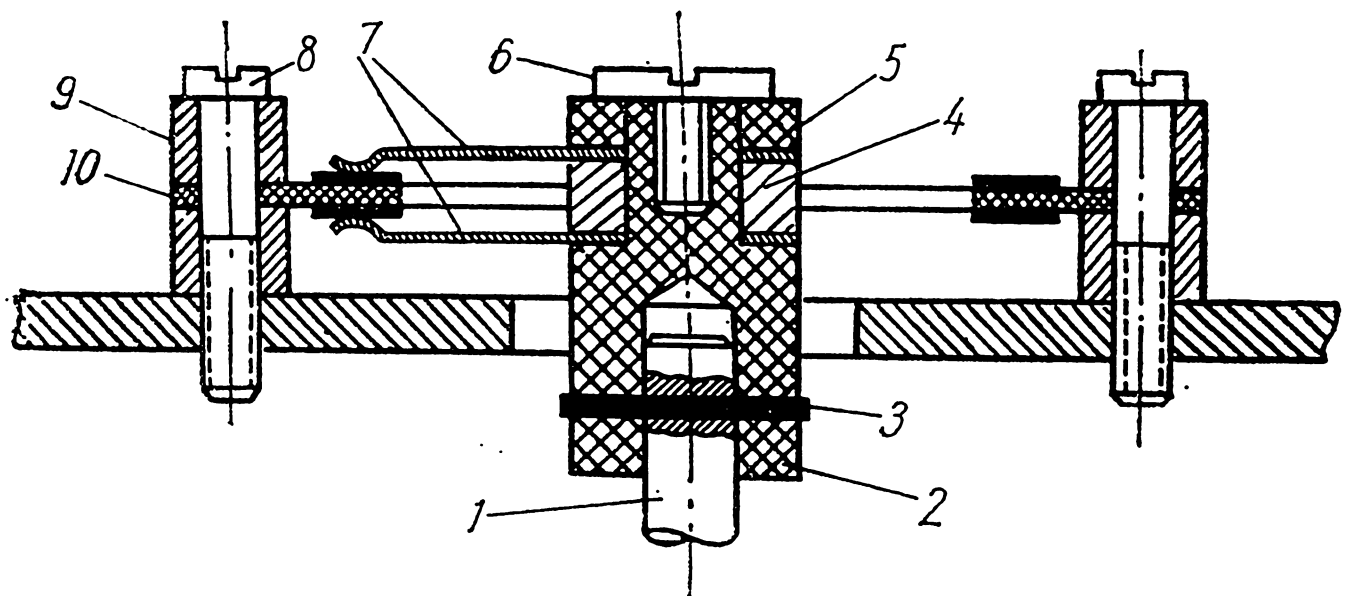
Механізм комутатора: 1 — вісь редуктора електродвигуна; 2 — ізоляційна насадка; 3 — шпонка; 4 — металеве кільце; 5 — текстолітова шайба; 6 — гвинт; 7 — пружини від контактів реле; 8 — кріпильний гвинт; 9 — втулка сталевая; 10 — плата комутатора.
